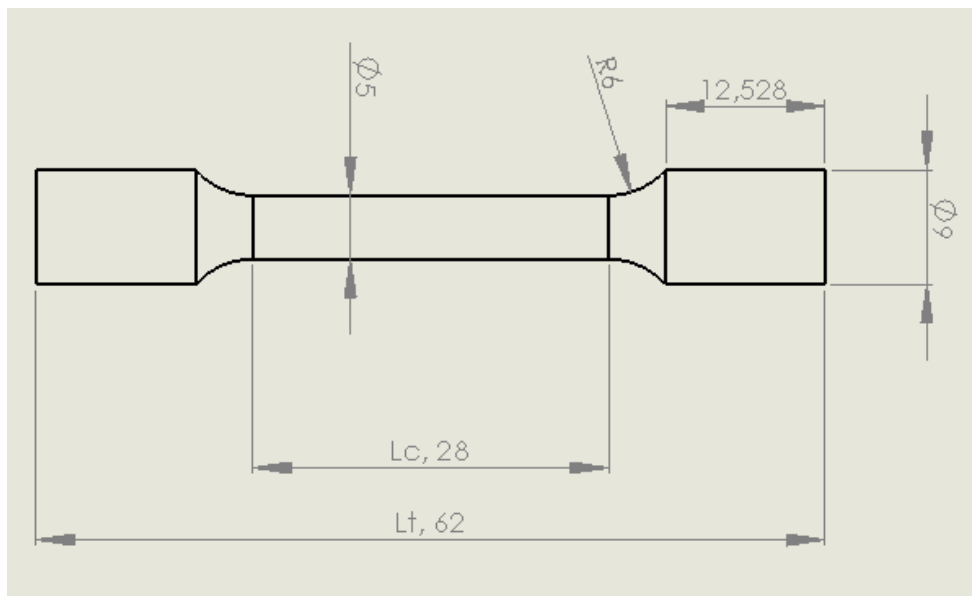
Geometría y dimensiones en mm de las probetas de tracción.
